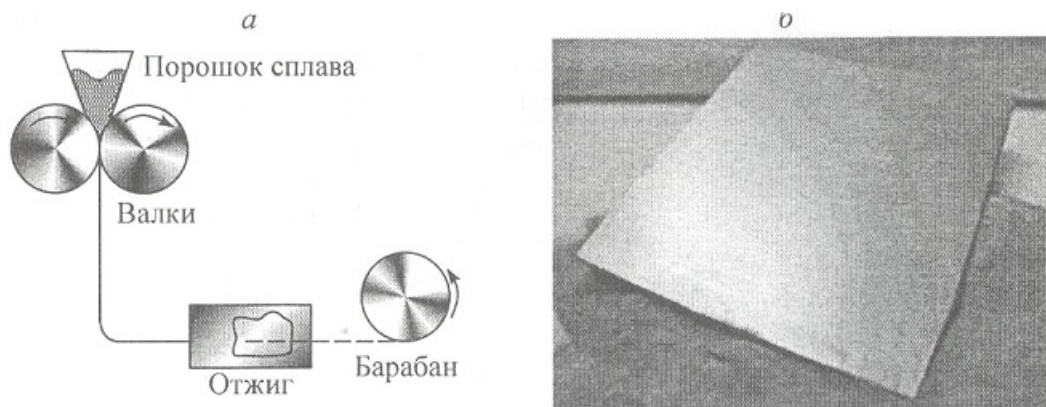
Схема валковой прокатки порошка (а) и лист прокатанного из порошка металла (б)
